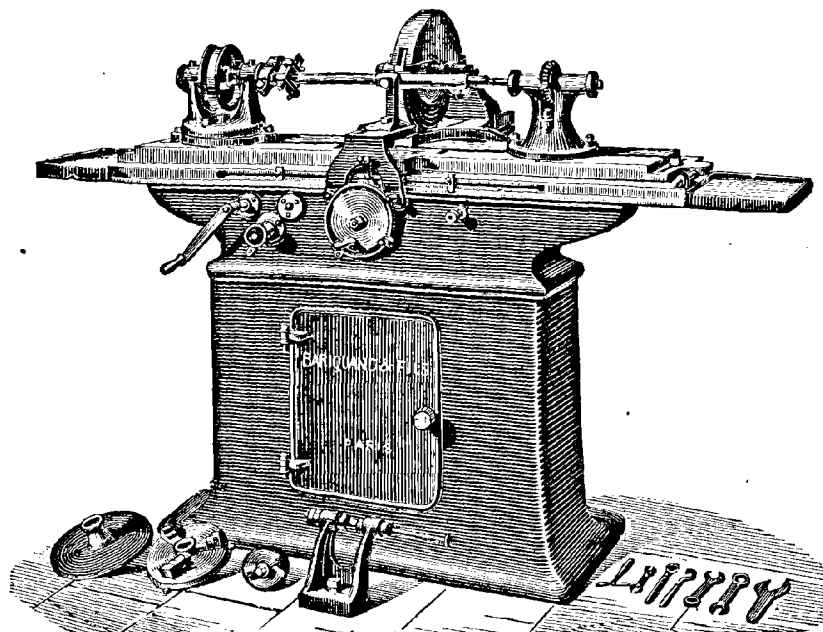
Machine à rectifier les pièces trempées de Bariquand et Marre.
